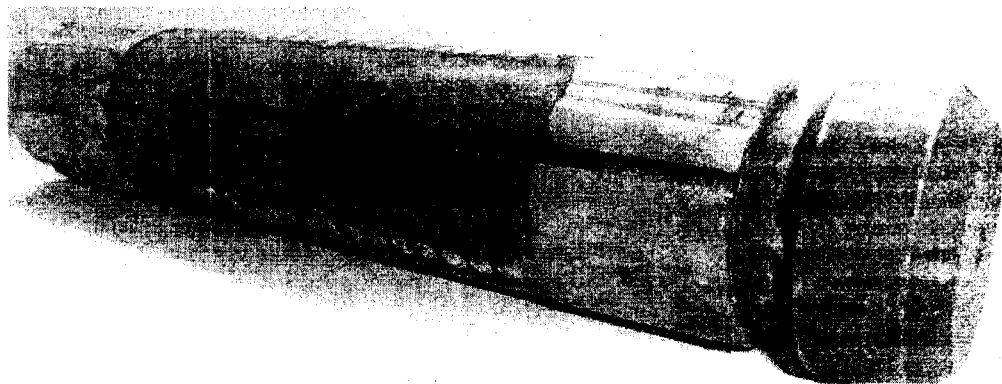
Комбинированный инструмент для обработки отверстий с прямой осью
